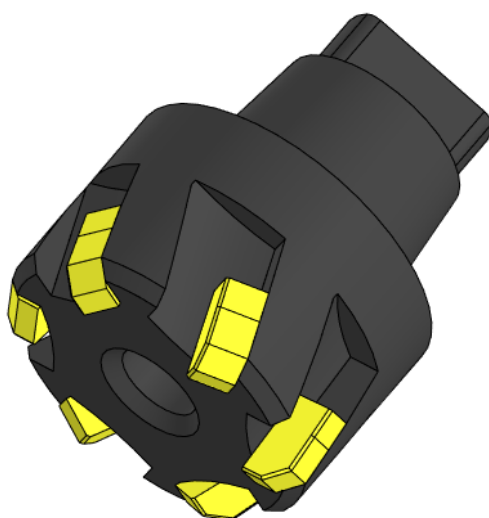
Твердосплавна головка для розвертання CoroReamer 830
